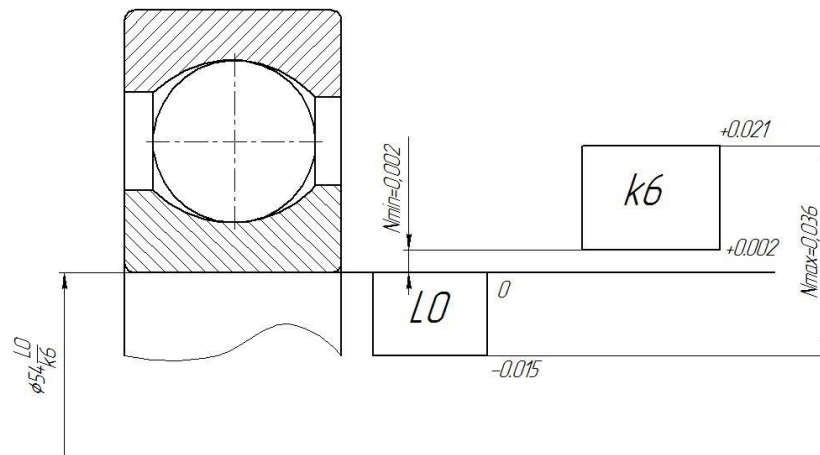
Расположение полей допусков в посадке подшипника на вал.
